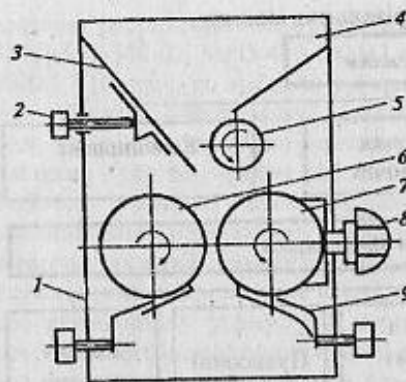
Вальцовий механізм МДП-II-1: 1 – корпус; 2 – гвинт; 3 – шибер; 4 – бункер завантажувальний; 5 – валок живильний; 6, 7 – валки розмелювальні; 8 – рукоятка; 9 – скребок
